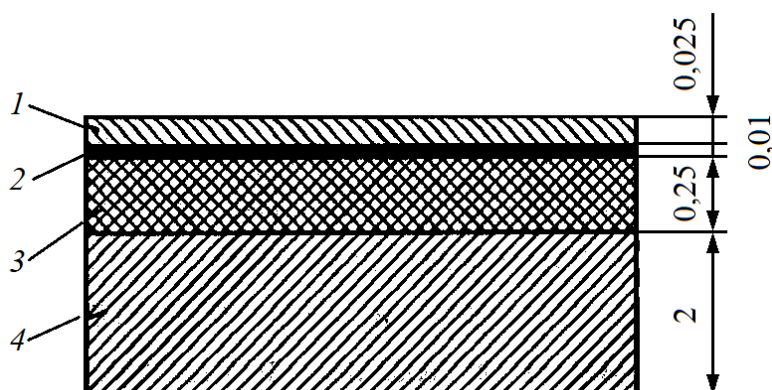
Схема строения четырехслойного металлического подшипника скольжения: 1 – сплав свинца и олова; 2 – никель; 3 – свинцовистая бронза; 4 – сталь
